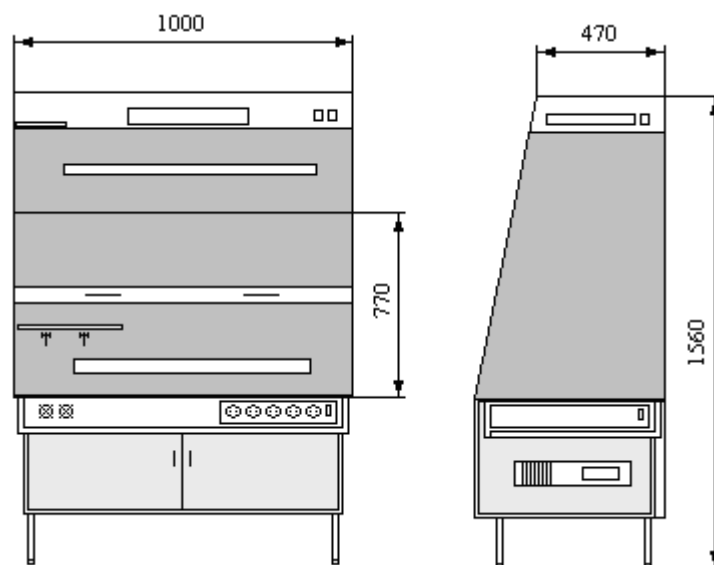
Витяжна шафа для виготовлення печатних плат
